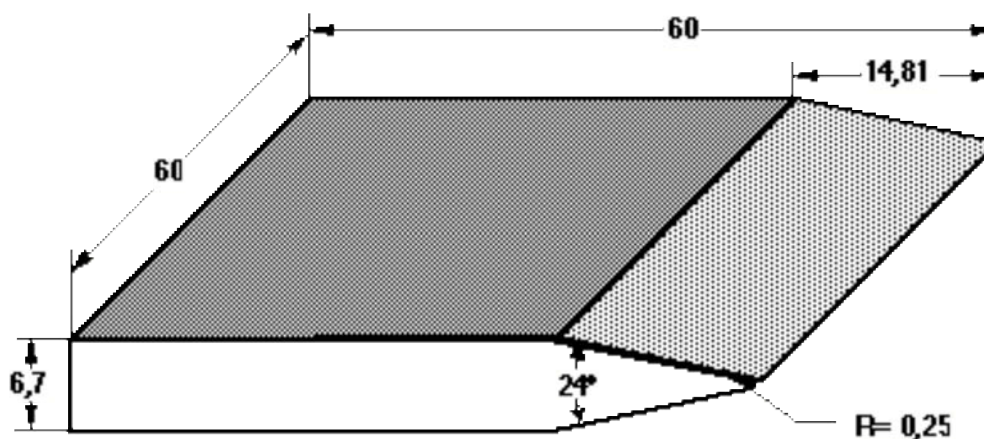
Schéma et dimension de l'éprouvette lisse de fatigue thermique
